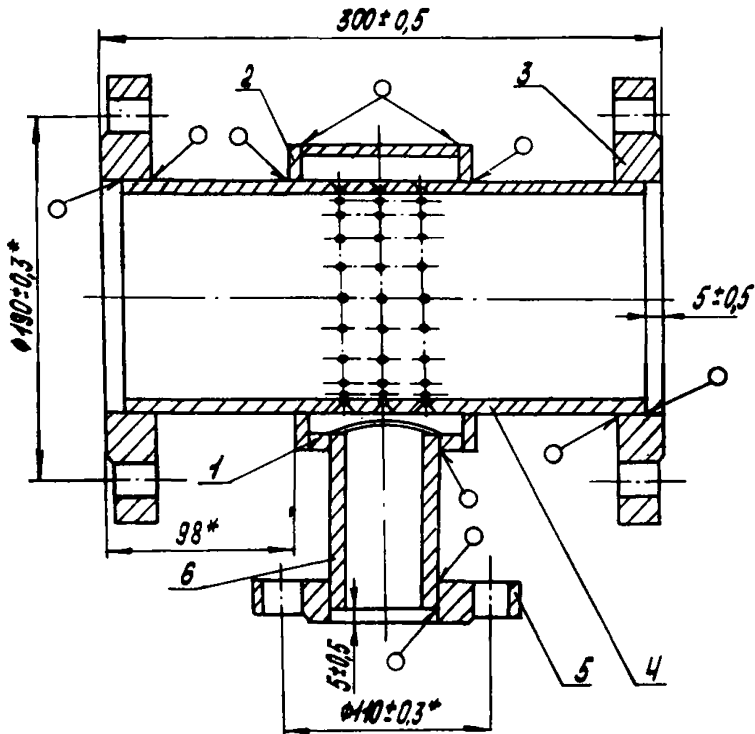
Ввод (сборочный чертеж). Сварные швы по ГОСТ 16037-80:
